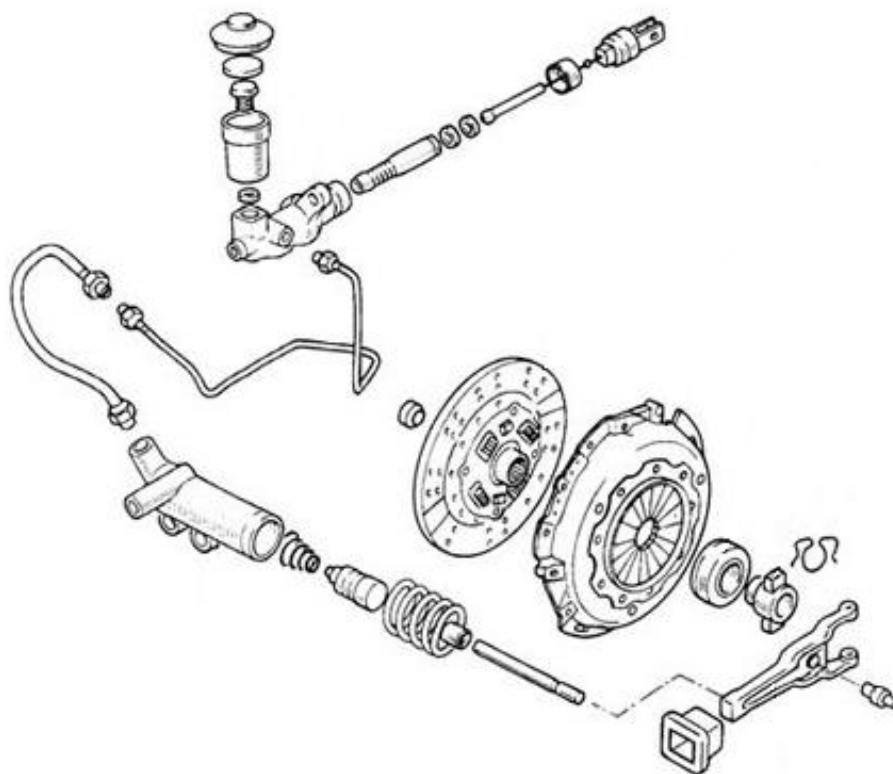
Despiece del mecanismo hidráulico de control de embrague
